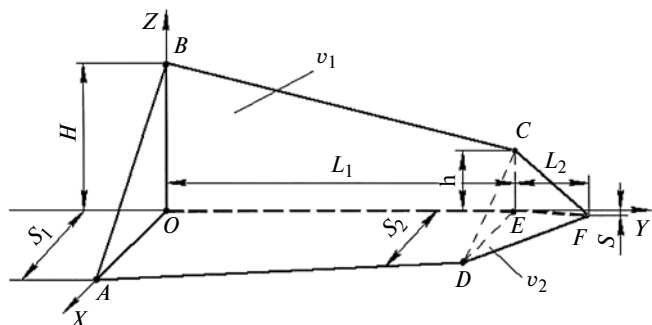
Форма и расчетные параметры заготовки клинка ножа
